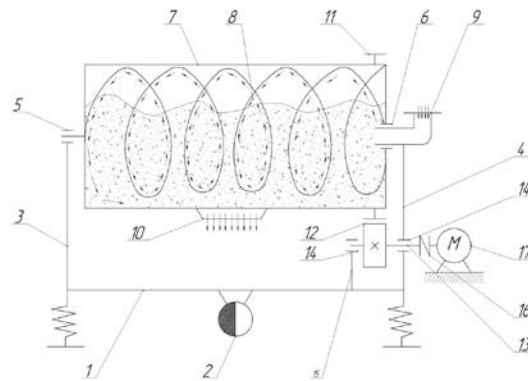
Принципова схема вібровідцентровго змішувача: 1 - підпружинена платформа; 2 - вібропривод; 3,4, 15 - стійки; 5, 6, 14 - підшипникові вузли; 7 - циліндричний контейнер; 8 - інтенсифікатор; 9,10 - патрубки для завантаження та розвантаження; 11 - зубчатий вінець; 12 - шестерня; 13 - приводний вал; 16 - еластична муфта; 17 - електродвигун
